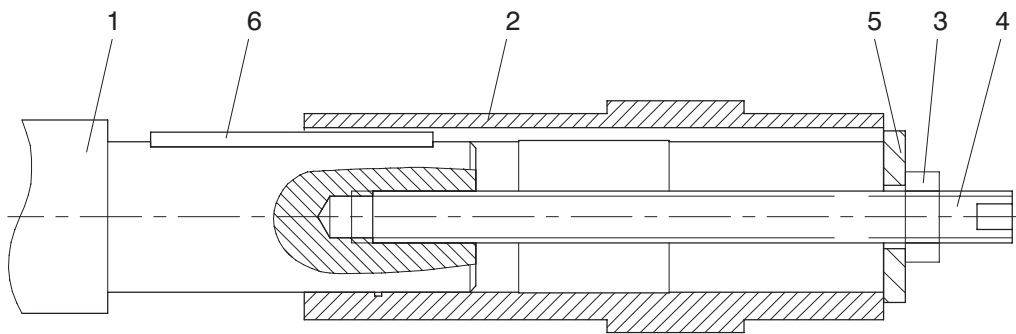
1: Montaggio dell'albero cavo e della linguetta
